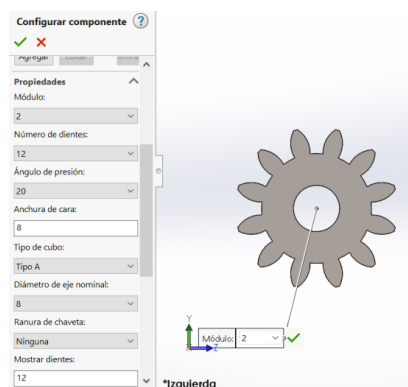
16. Engranaje de la pieza acoplada al servomotor
